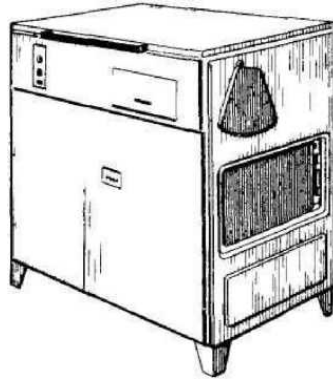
Установка ОРГ-4990Б-ГОСНИТИ для миття деталей
